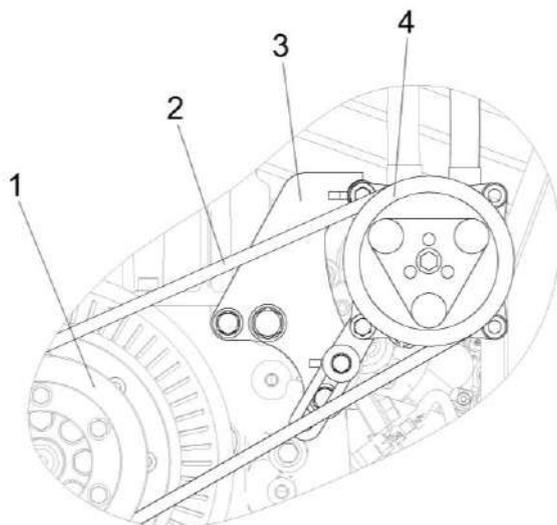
Регулировки ременной передачи привода доизмельчающего устройства
